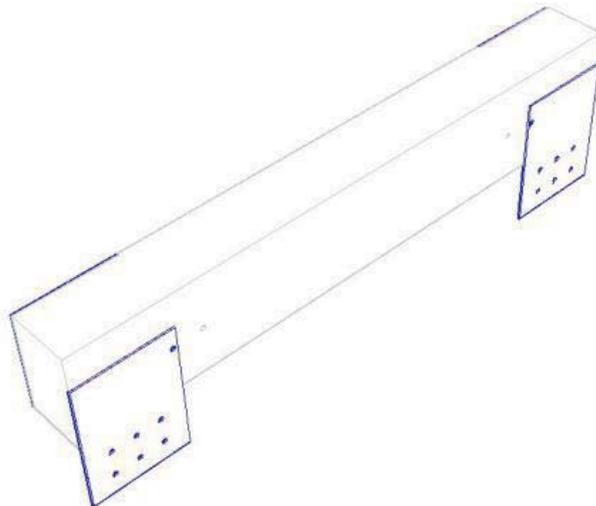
Ensemble de chargement à trois pièces – poutre horizontale
